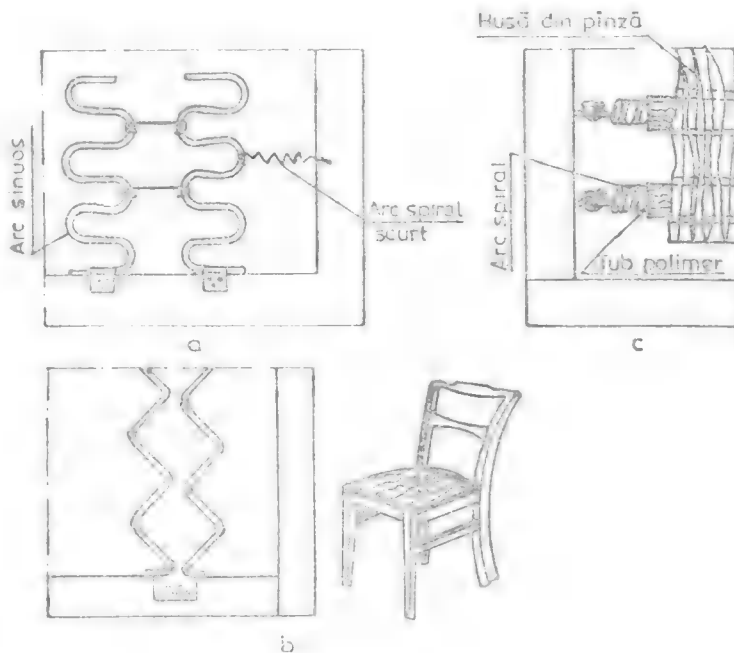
Fixarea arcurilor dispuse în plan orizontal.
